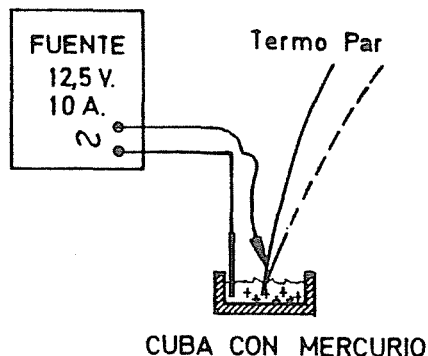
Esquema de la soldadura por descarga eléctrica.
